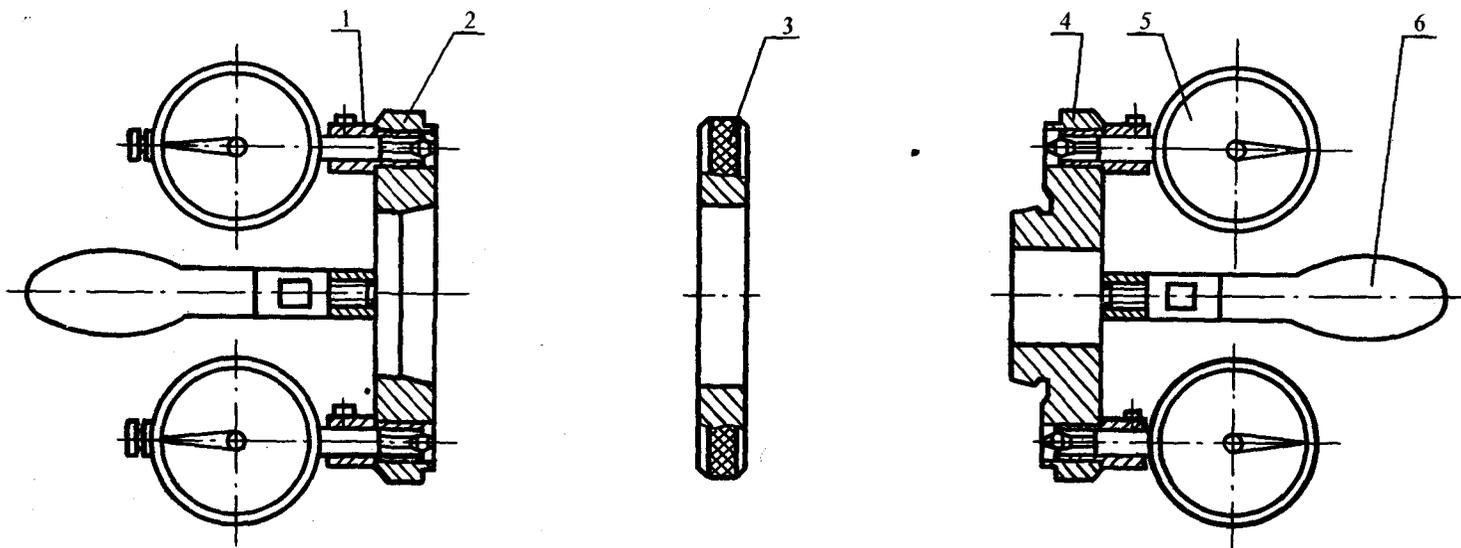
Приспособление для контроля конусных посадочных поверхностей фланцев шпинделей:
